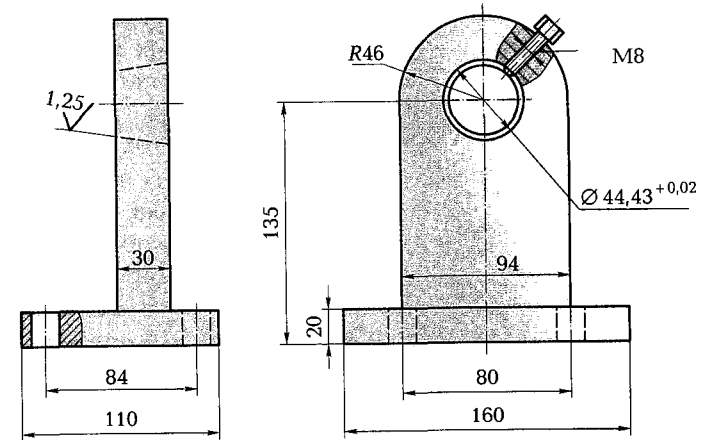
Чертеж приспособления для сборки инструментальной оправки
